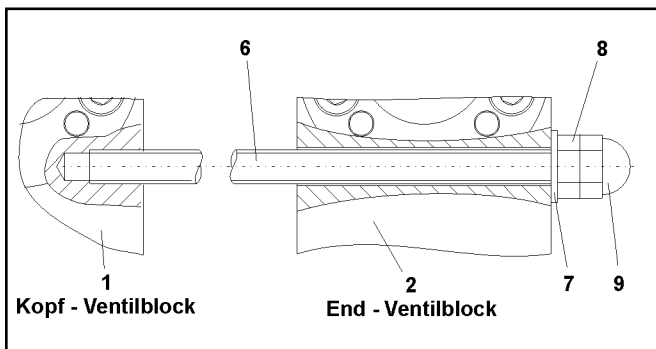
Gewindestangen => Stückliste siehe Tabelle 1 auf Seite 2
